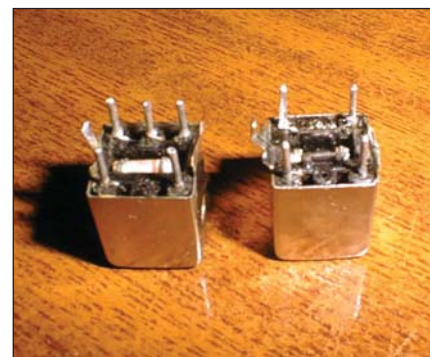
Antes de montar la bobina, deberemos localizar el pequeño condensador tubular que poseen en la parte inferior (izquierda) y romperlo con ayuda de un pequeño destornillador u objeto punzante (derecha).
